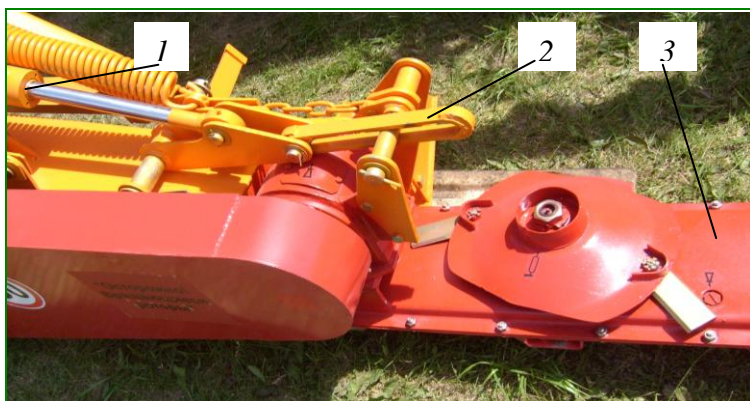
Вид шарнирного устройства косилки АС-1.
